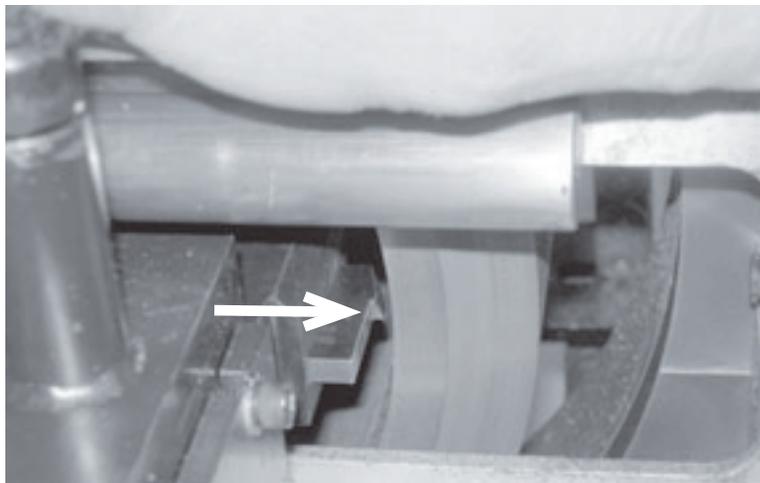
Stellen Sie sicher, dass sich das Werkzeug innerhalb des Rohrinnehdurchmessers befindet, bevor der Außenwerkzeugschlitten in das Rohr bewegt wird.
